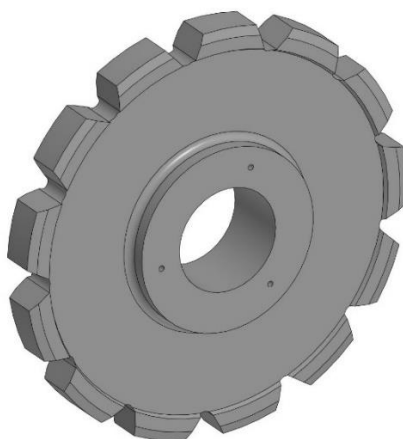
3D-модель деталі «Зірочка»
